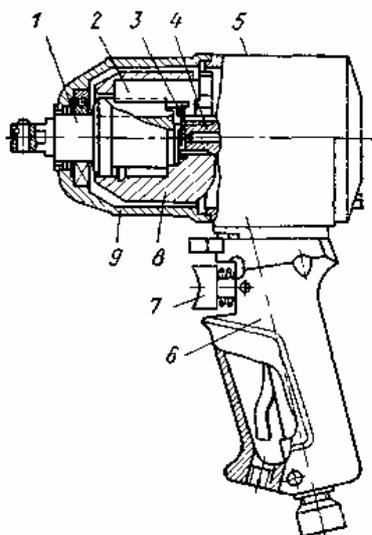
Гайковерт пневматический ударного действия: 1 – шпindelь; 2 – кулачек; 3 – пружина; 4 – ротор; 5 – корпус; 6 – рукоятка; 7 – кнопка; 8 – маховик; 9 – кожух
